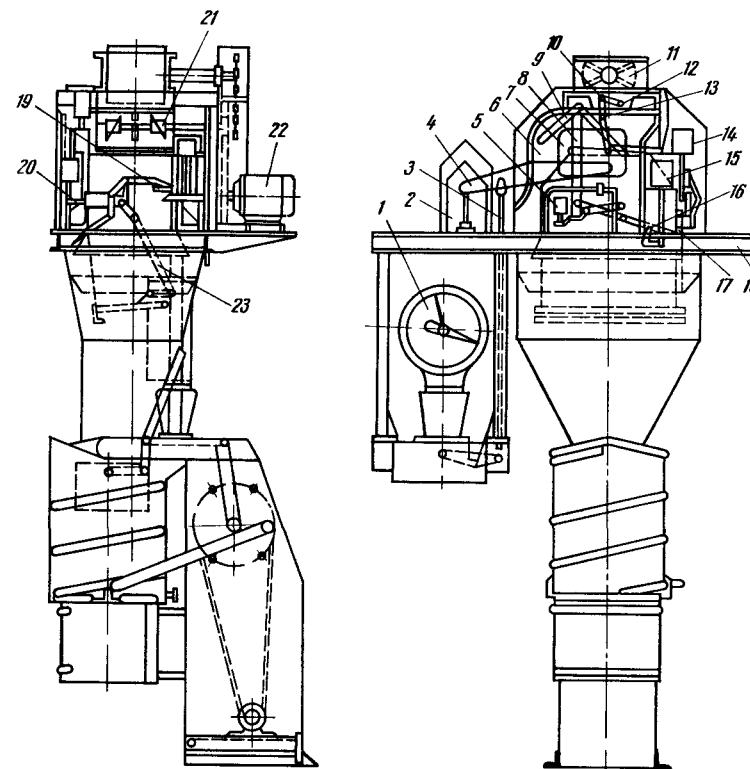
Полуавтоматический весовой дозатор ДВМ-75
